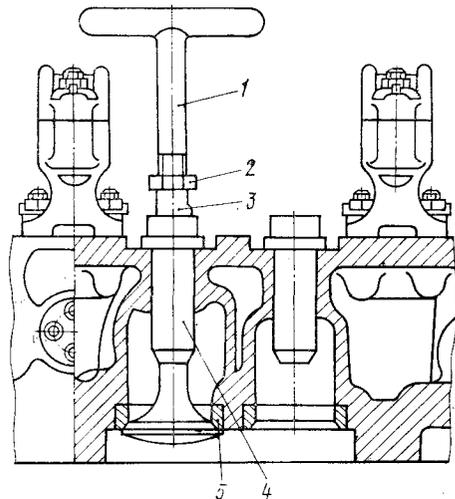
Приспособление для притирки клапанов: 1 — приспособление; 2 — гайка; 3 — клапан; 4 — направляющая клапана; 5 — седло клапана
